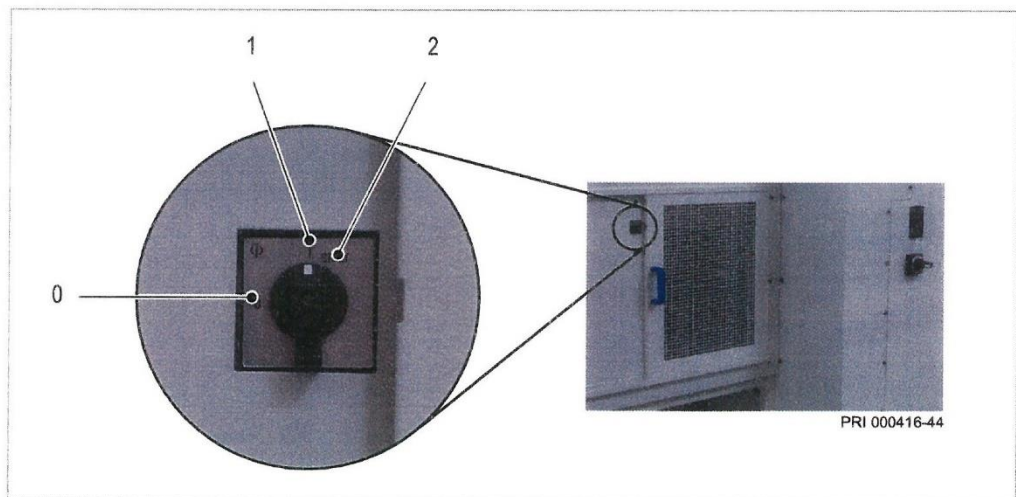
Drehschalter Werkzeugwechslers Tür
